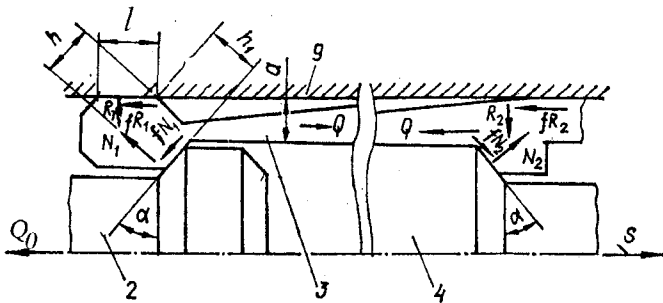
Розрахункова схема для визначення сил затискання інструмента
